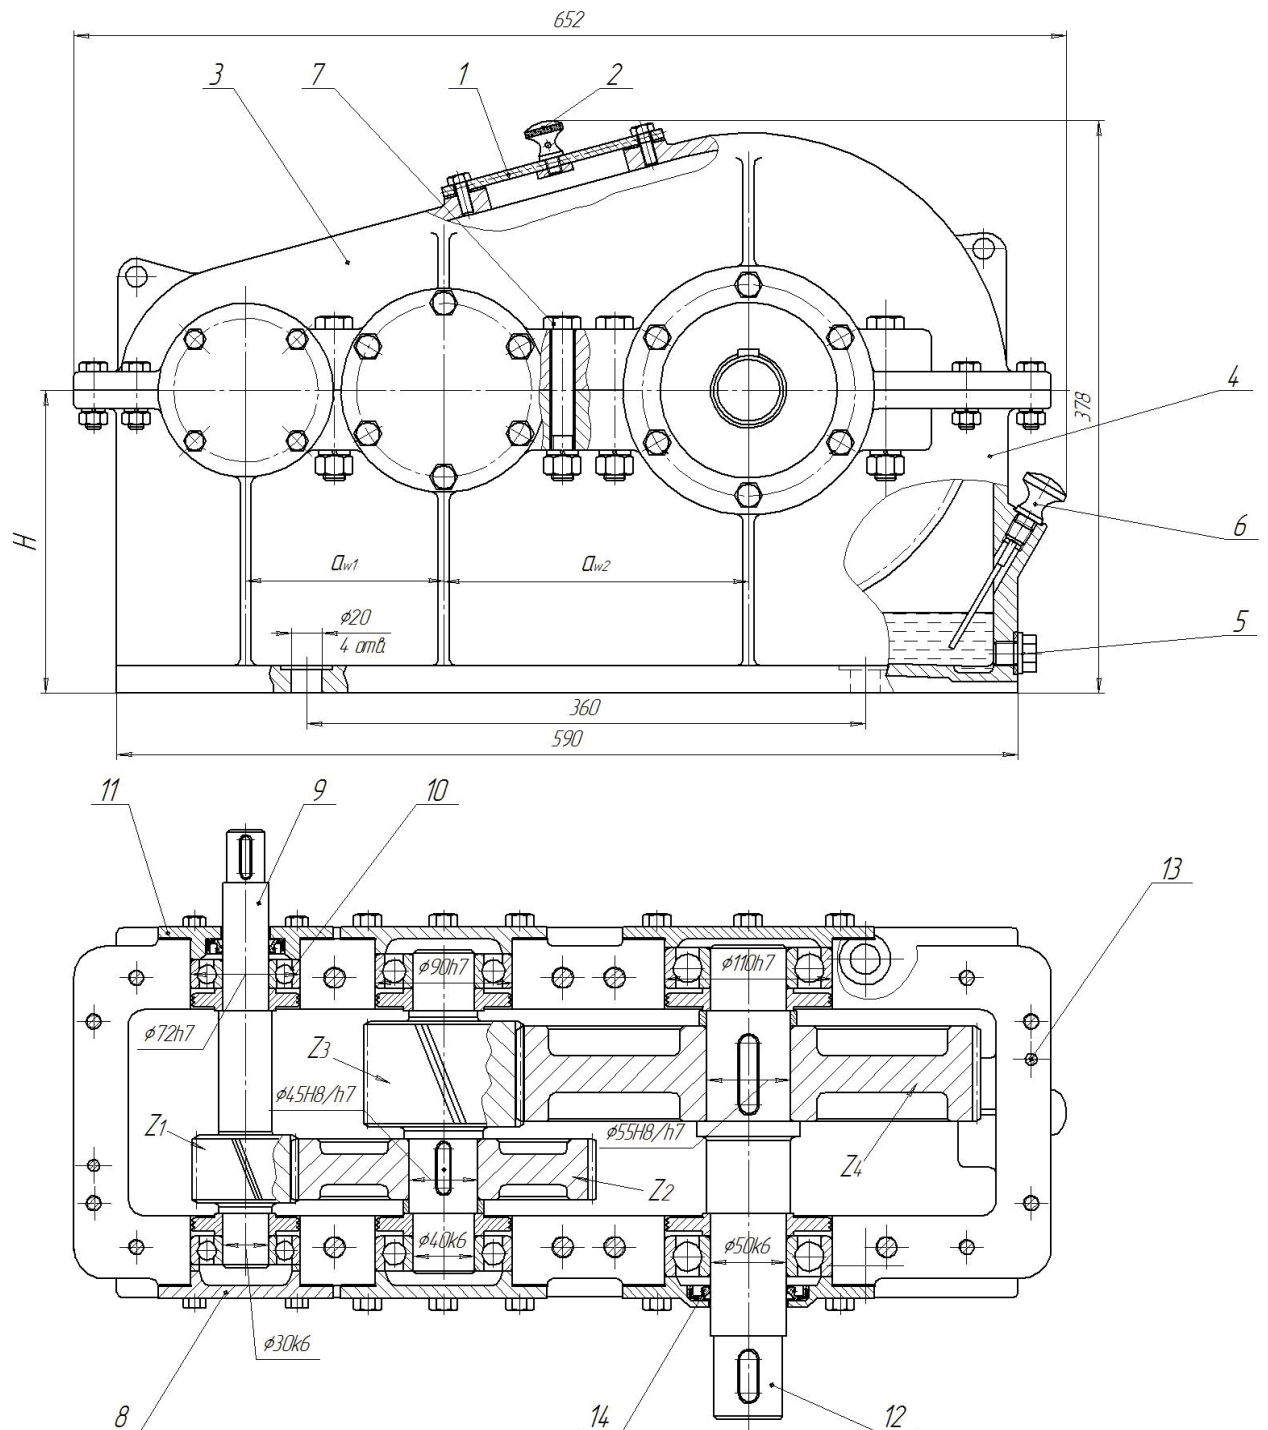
Редуктор циліндричний двохступінчастий
